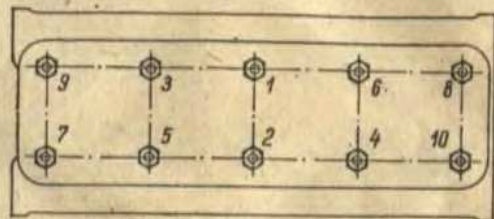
Порядок затяжки гаек головки цилиндров двигателей ЯАЗ-М204
